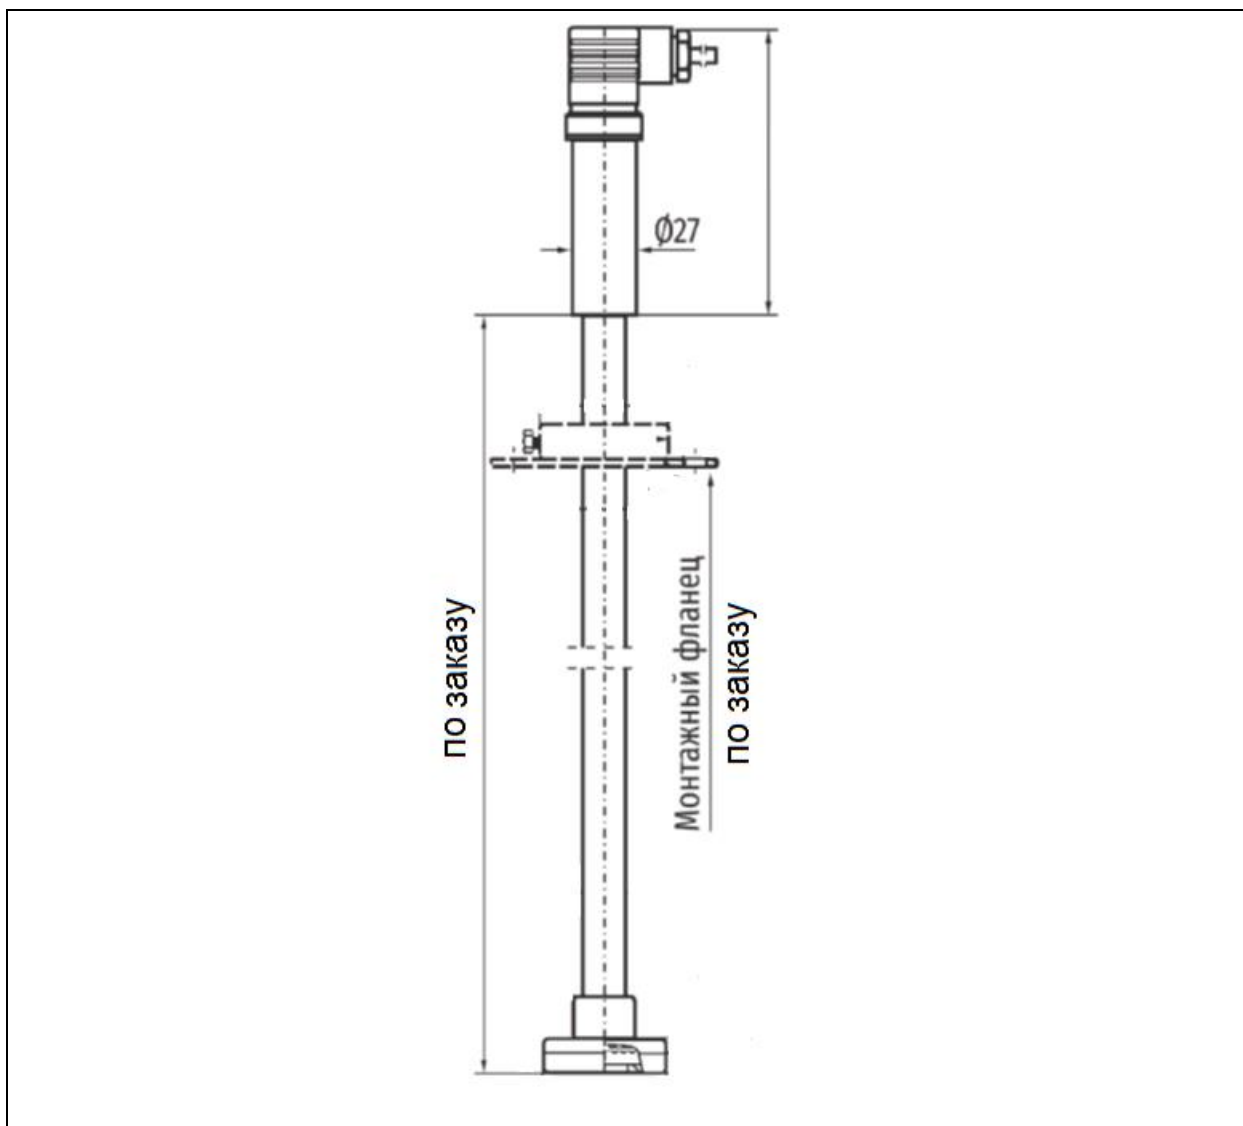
Внешний вид и габаритные размеры преобразователя РС-28Р с исполнением корпуса РД
